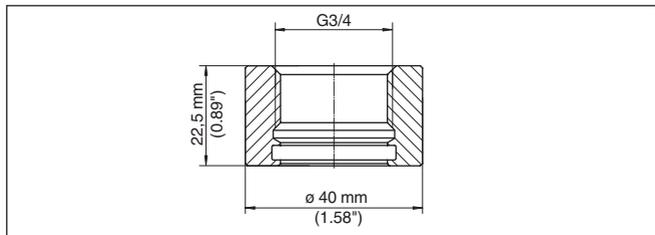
Dimensiones racor para soldar G $\frac{3}{4}$ (DIN 3852-X) - VEGABAR 82
